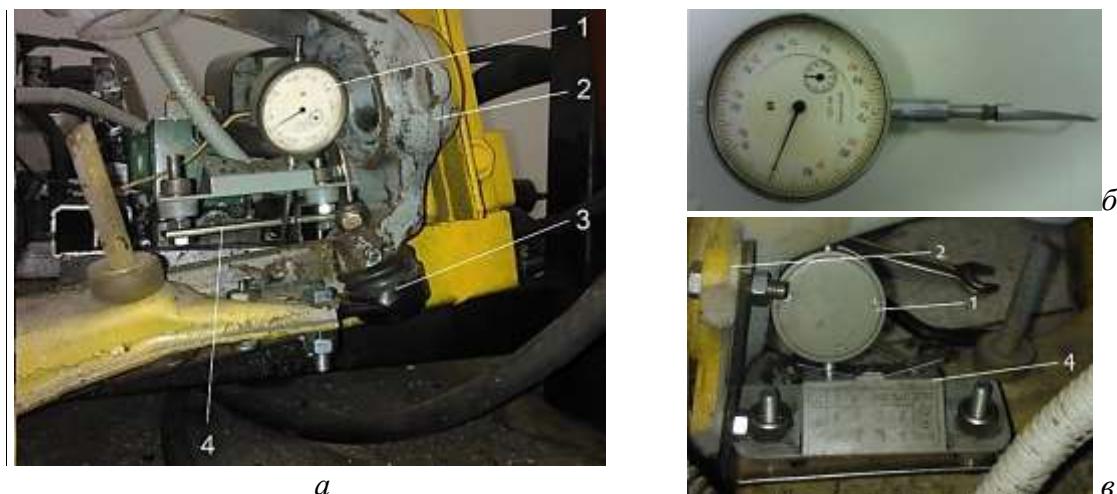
Устройство для определения осевого зазора в шарнирном соединении механическим способом: а - установка устройства на легковом автомобиле; б - общий вид индикатора часового типа ИЧ-10; в - измерительное устройство ви - вид сзади; 1 – индикатор часового типа ИЧ-10; 2 – поворотный кулак передней подвески, 3 – исследуемый элемент – шаровый шарнир, 4 – кронштейн установки индикатора ИЧ-10
